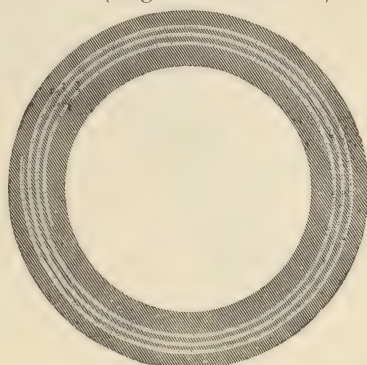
Schlauch mit 33 mm Innendurchmesser, 7 mm Wandstärke, 3 Einlagen
